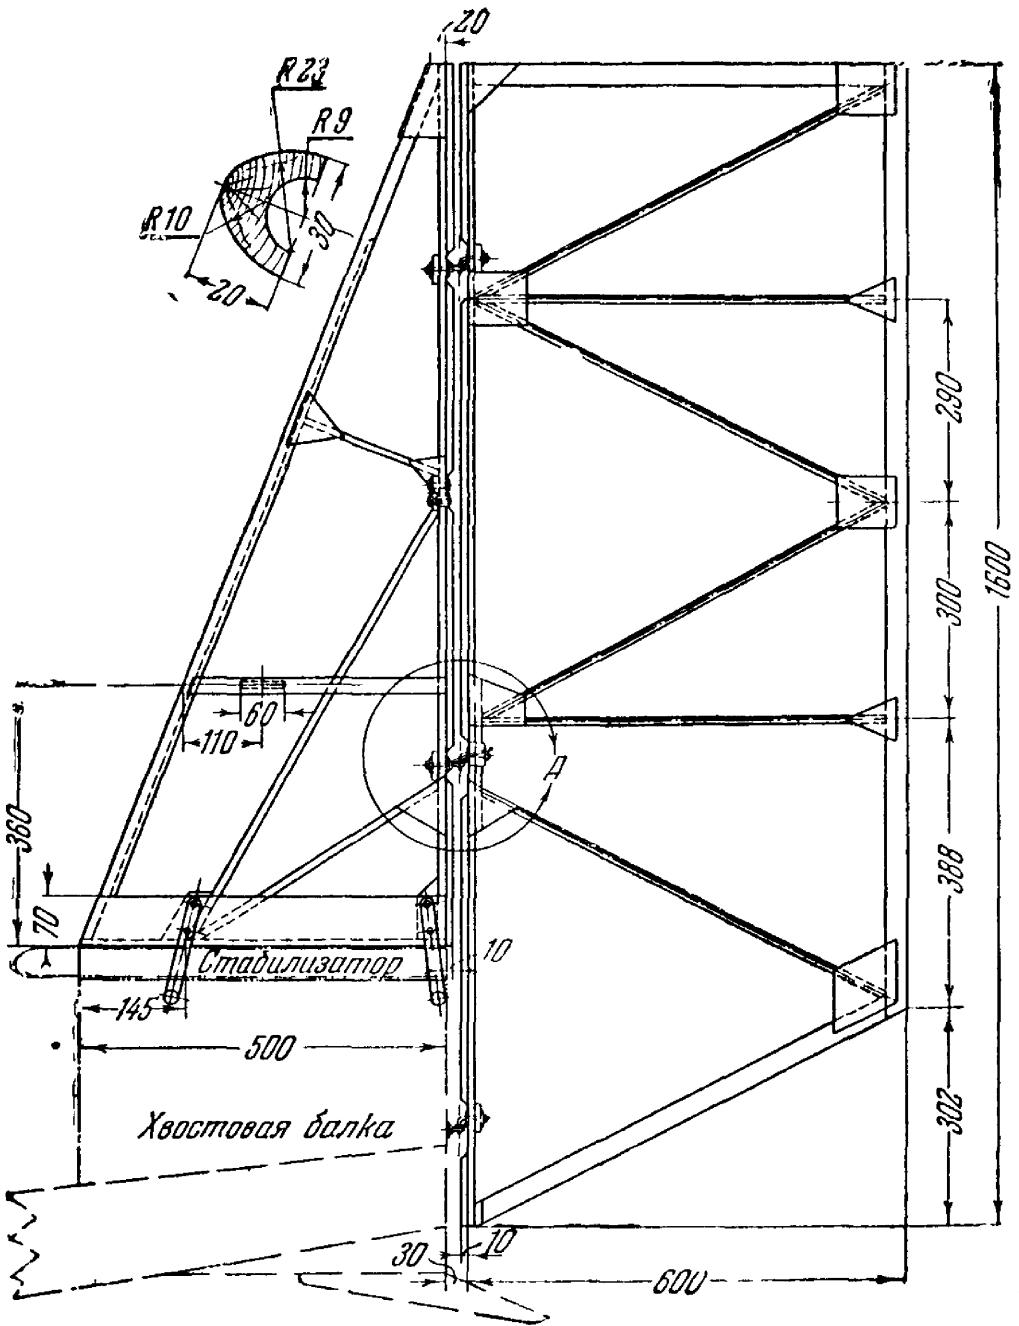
Планер А-1 Верткальное оперение и подкос оперения
